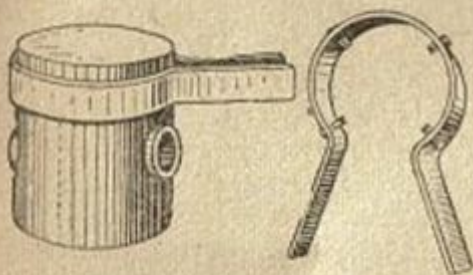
Приспособление для очистки канавок колец в поршне от нагара
